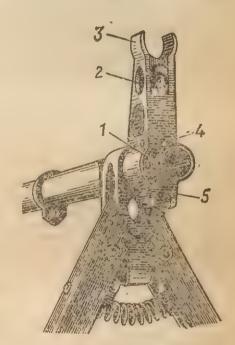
Основание мушки: 1 — резьба; 2 — отверстие для 3 - предохранитель полозка; 4 - фиксатор: 5 - упор мушки; для шомпола
